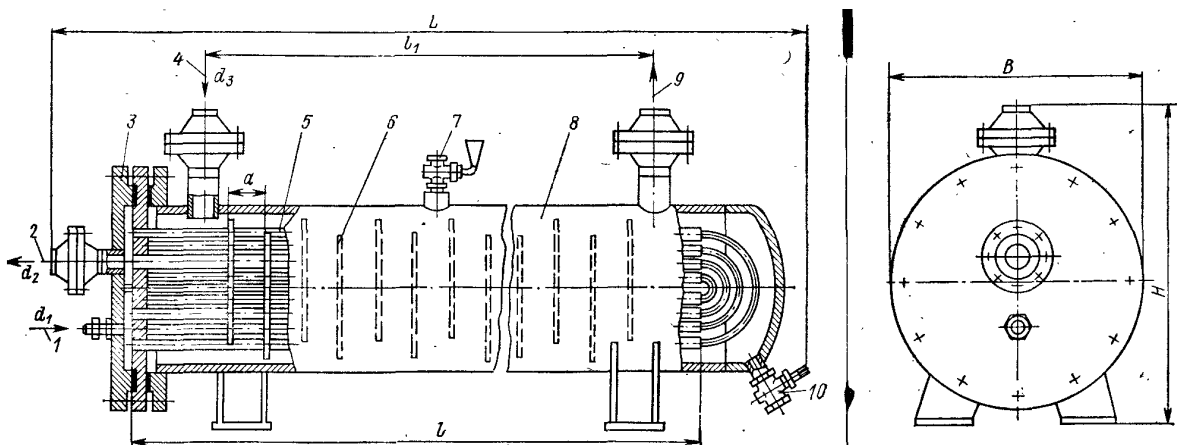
Кожухотрубний випарник з кипінням робочої рідини всередині U-образних труб: 1,2- вхід і вихід робочої рідини; 3- кришка; 4,9- вхід і вихід розсола; 5- кипятильні труби; 6- перегородки; 7- вентиль для продувки; 8- кожух; 10- злив розсолу
